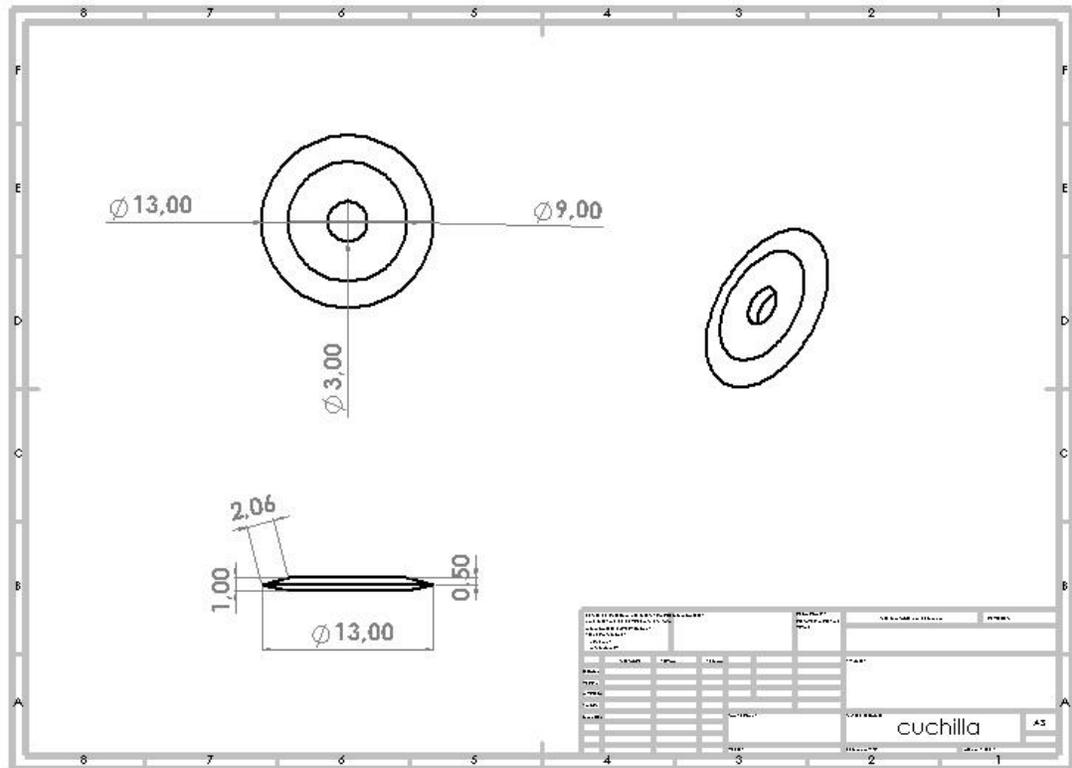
Vista isométrica del disco de corte [Elaboración propia].
